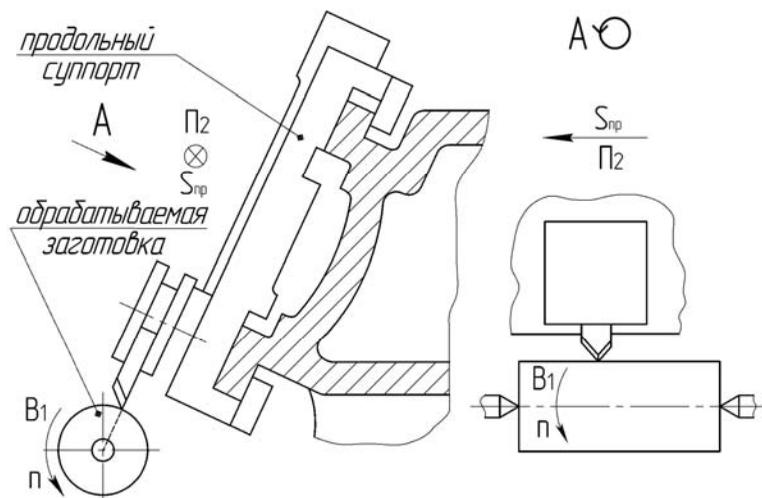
Рабочая зона токарного гидрокопировального полуавтомата и формообразующие движения при обработке участка заготовки с цилиндрической поверхностью с продольной подачей продольного копировального суппорта
